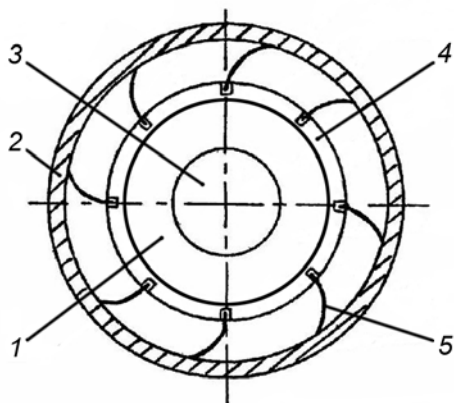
Конструкция с защитным кожухом: 1 – пьезоэлемент; 2 – статор; 3 – вал; 4 – защитный кожух; 5 – толкатели
